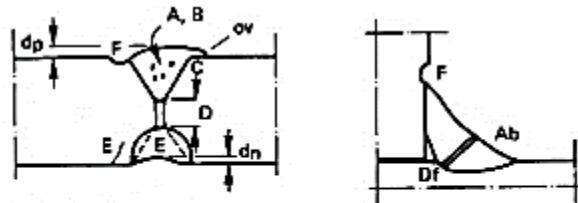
Tipos de defectos de soldadura
